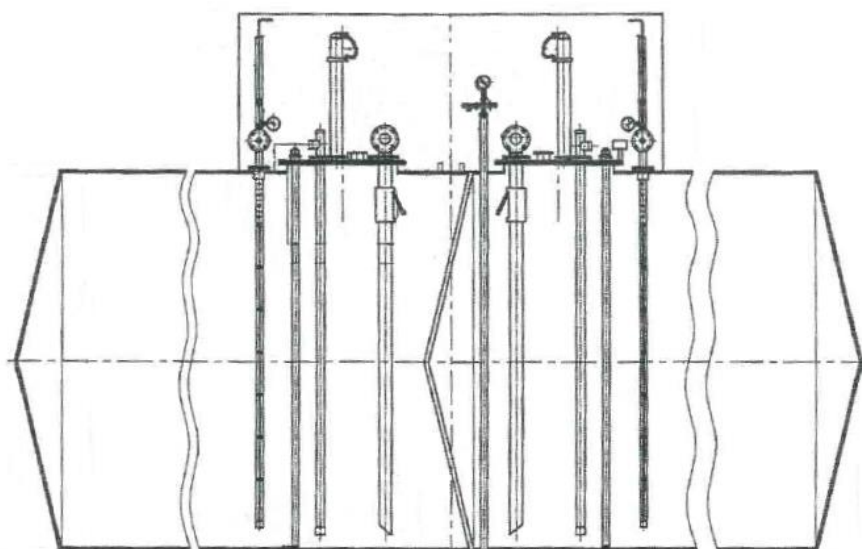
Общий вид эскиза резервуаров РГС-50
